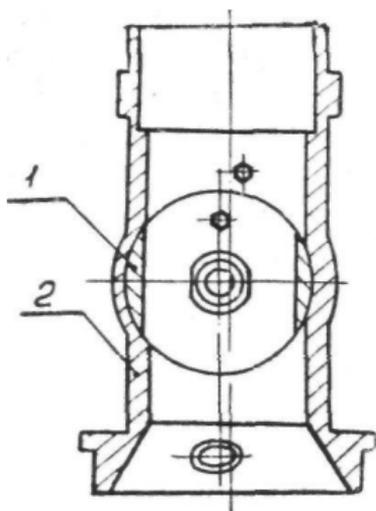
Положение вставки в корпусе карбюратора, вызывающее неравномерную работу цилиндров двигателя ИЖ-Ю.
